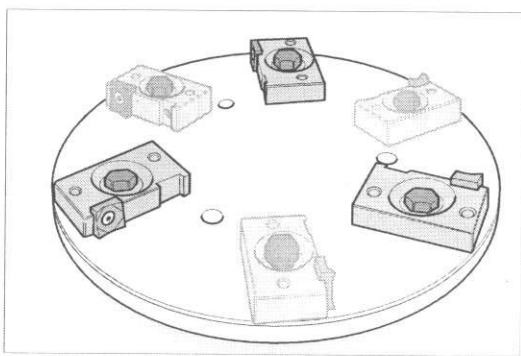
Vous pouvez équiper le disque de fraisage de 3 et 6 éléments de maintien. Chaque élément doit au moins supporter une plaque réversible.
